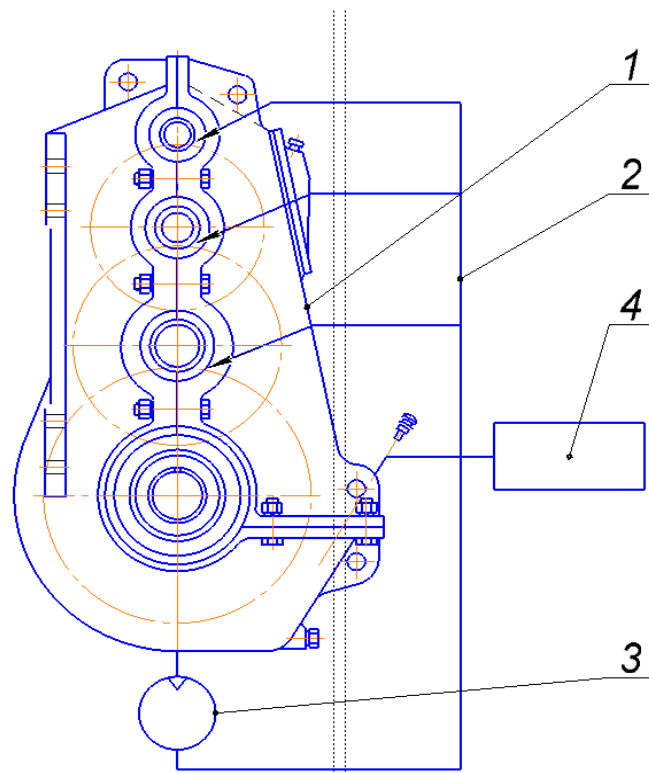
Устройство для струйной смазки вертикального трехступенчатого редуктора:
